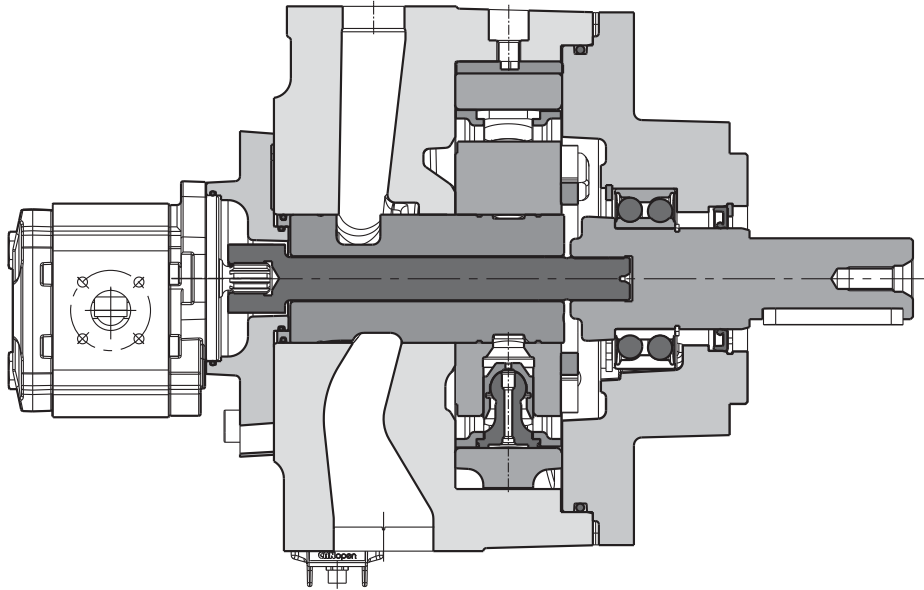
Radialkolbenpumpe mit angebaute Zahnradpumpe mit SAE-A-Adapter
